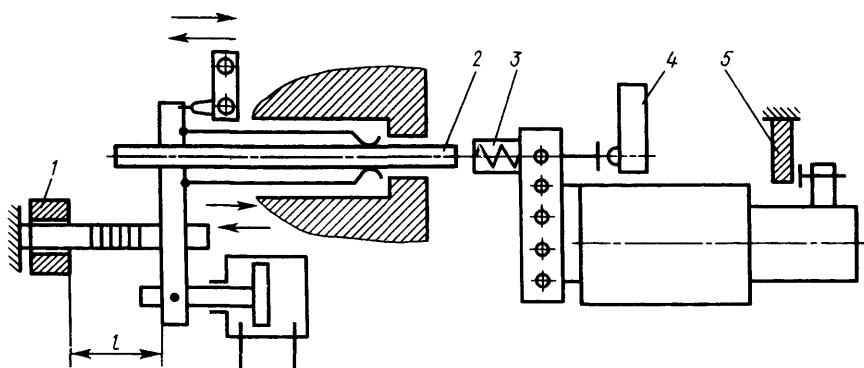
Схема регулировки угла подачи и контроля наличия прутка
